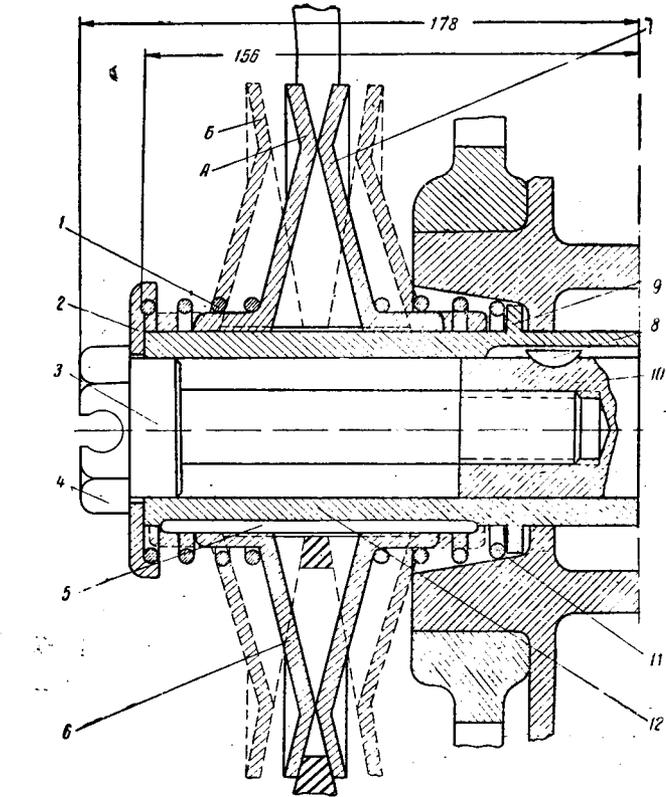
Схема устройства для бесступенчатого регулирования оборотов вентилятора и водяного насоса двигателя Д-36:
